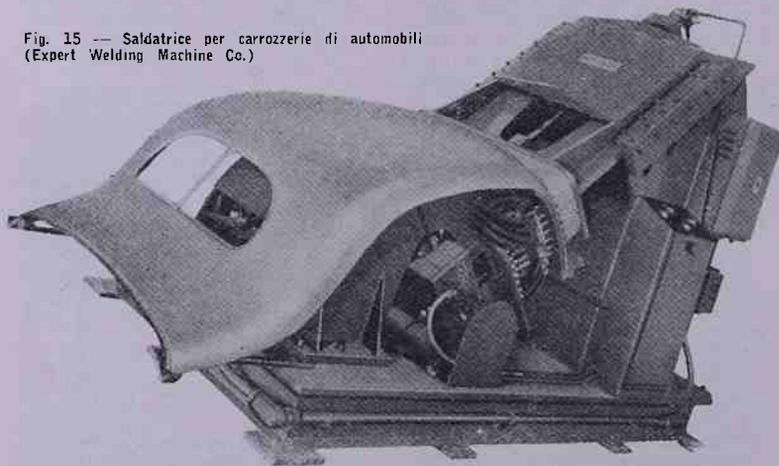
Saldatrice per carrozzerie di automobili (Expert Welding Machine Co.)
